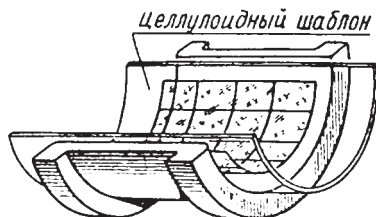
Проверка качества шабрения рабочей поверхности подшипника
